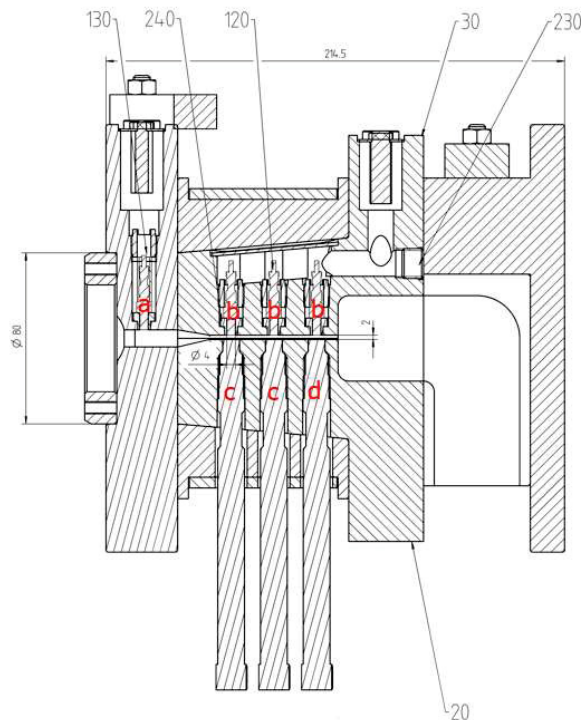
Längsschnitt des DESMA Elastomerspritzgießmaschinenrheometers:
